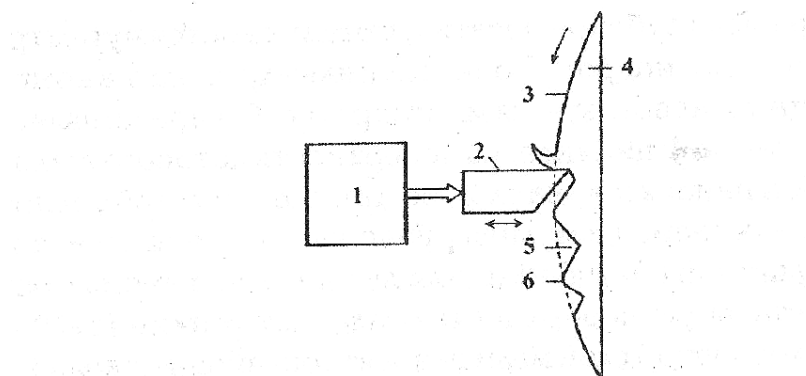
Схема электронно-механического гравирования: 1 — система электродного управления движением резца; 2 — резец; 3 — поверхность формного цилиндра; 4 — формный цилиндр; 5 — печатающий элемент (ячейка); 6 — пробельный элемент
